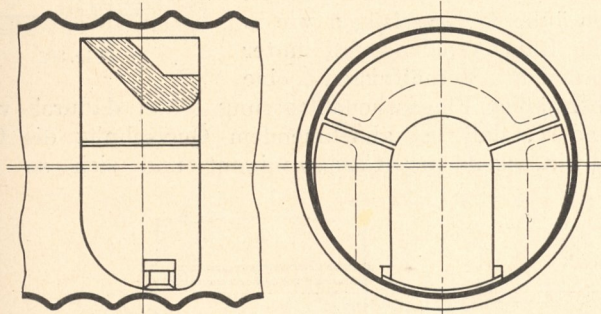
Flammrohreinsatz aus ff. Steinen. D. R. G. M. Nr. 190101. Ausführung: Dingersche Maschinenfabrik, A.-G., Zweibrücken.
